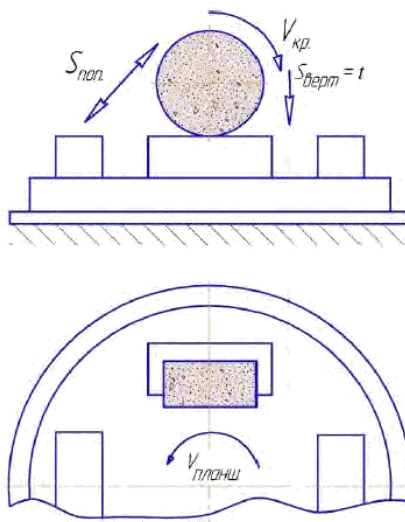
Схема плоского шлифования периферией круга на станках карусельного типа
